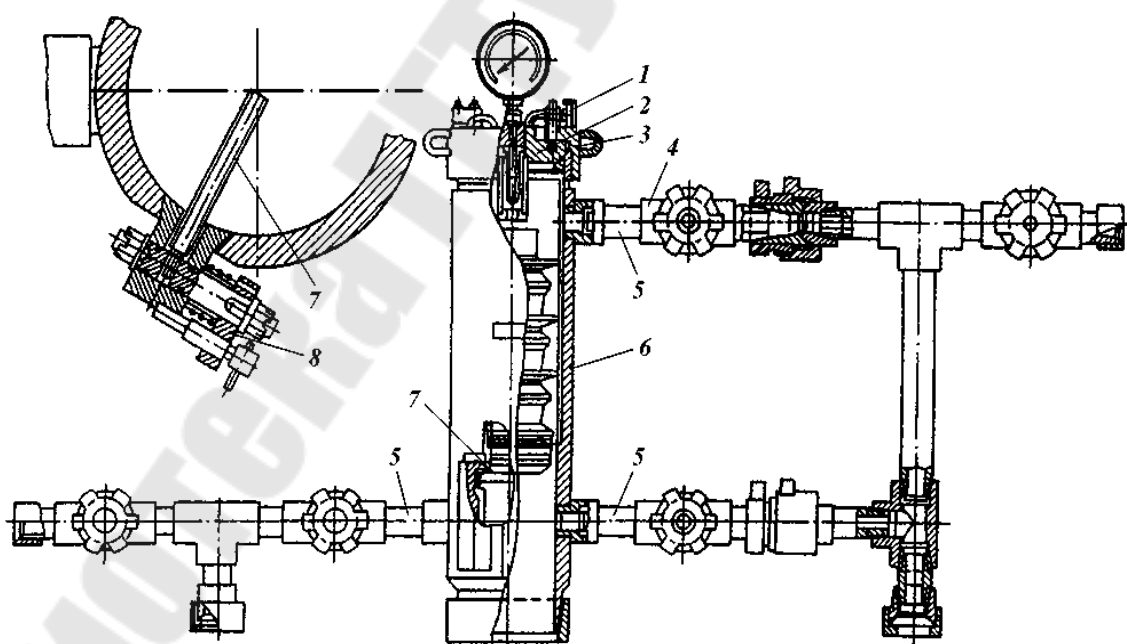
Универсальная цементируемая головка типа ГЦУ: 1 – съемник; 2 – крышка; 3 – гайка; 4 – проходной кран; 5 – присоединительные линии; 6 – корпус; 7 – фиксатор пробки; 8 – указатель (сигнализатор) начала движения пробки
